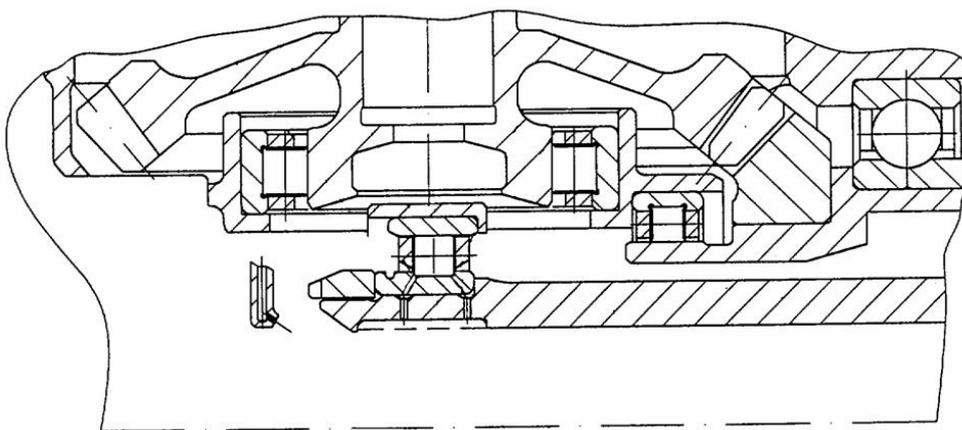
Подвод масла к опоре вала ГТД через форсунку и внутреннюю обойму подшипника
